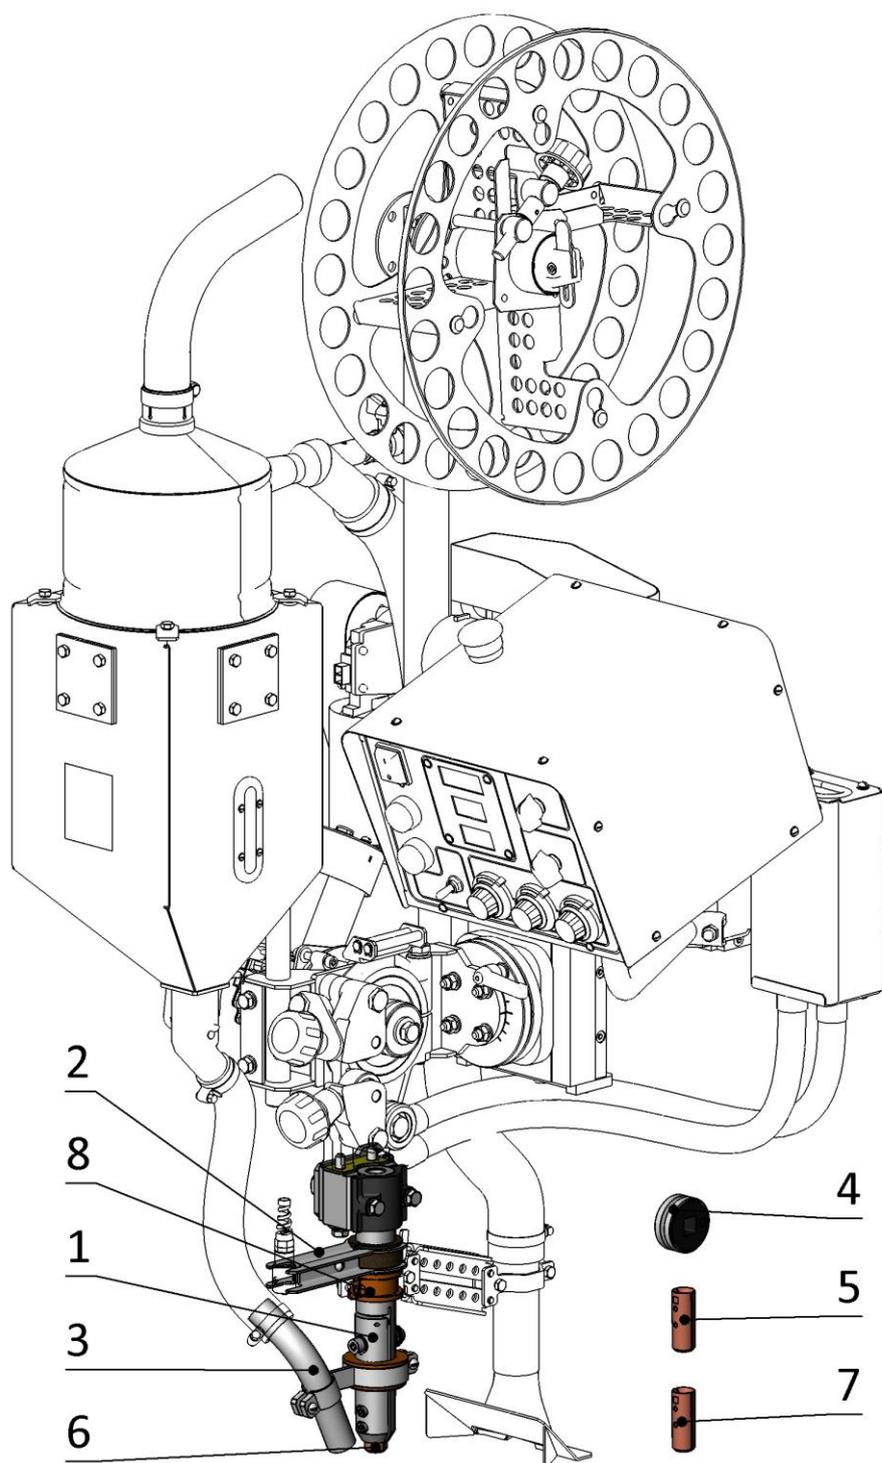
Комплект токоподвода D35 для сварки одной проволокой $\varnothing 3,0-5,0$ мм.
